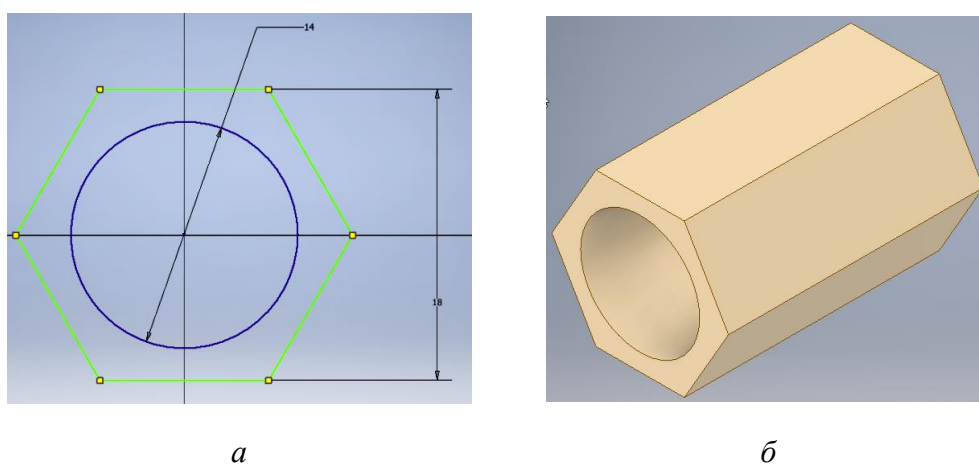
Эскиз (а) и 3D-модель (б) патрубка призматического
